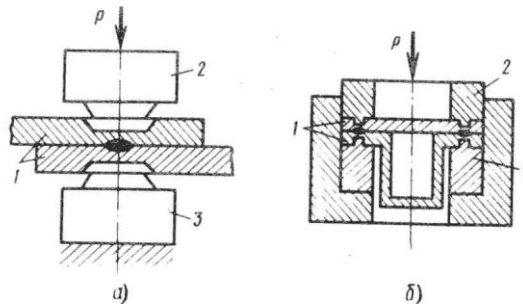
Холодная сварка: а — точечная; б — по контуру
